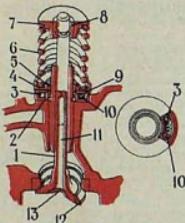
Механизм вращения выпускного клапана двигателя ЗИЛ-130: 1 — клапан; 2 — неподвижный корпус; 3 — шайба; 4 — упорная шайба; 5 — замочное кольцо; 6 — пружина; 7 — тарелка; 8 — стержень; 9 — цапфа; 10 — возвратная пружина; 11 — напрямое наполнение; 12 — жаропрочная наплавка; 13 — заглушка.
